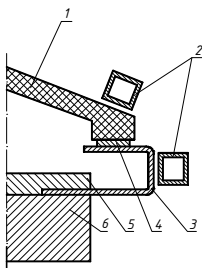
Схема нагрева проходным индуктором с двусторонним расположением токопроводов: 1 – прижим, 2 – прямой и обратный токопроводы,; 3 – контактодержатель, 4 – контактная пластина, 5 – зажимное приспособление, 6 – поворотный стол
